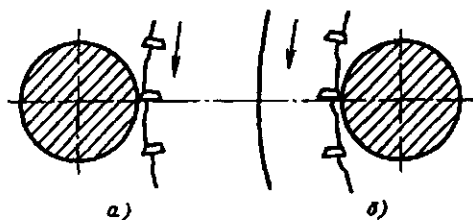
Схемы круглого фрезерования поверхностей тел вращения: а – внешним касанием; б – внутренним касанием
